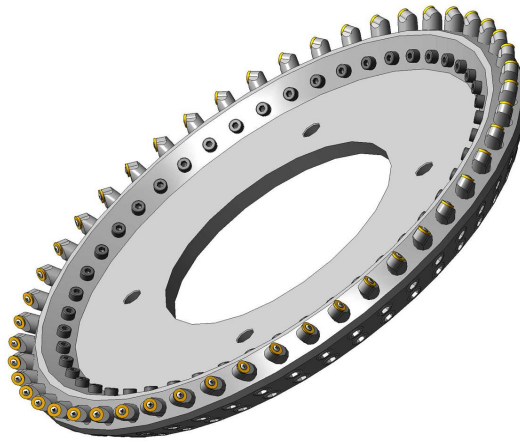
Торцева фреза з циліндричними різальними вставками та додатковими кріпильними гвинтами
